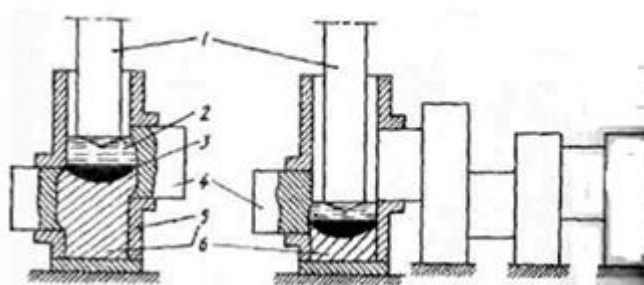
Схема получения заготовки коленчатого методом приплавления: 1- расходуемый электрод, 2- шлаковая ванна, 3- металлическая ванна, 4- приплавляемая заготовка шейки, 5- литейная форма, 6- отливка щеки.
